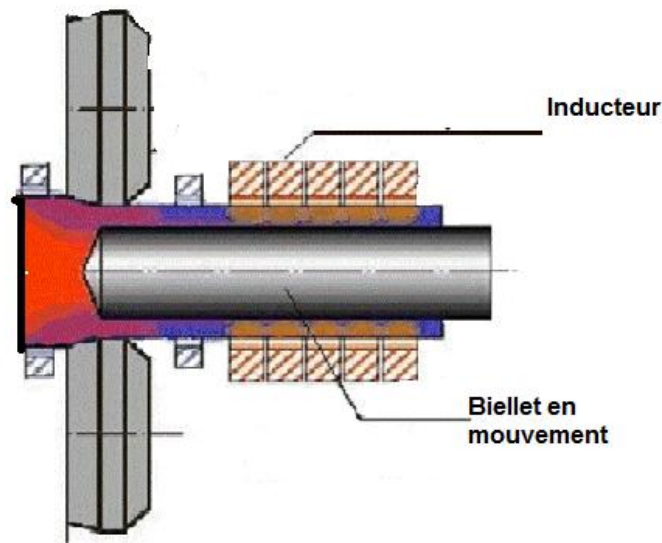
Chauffage avant formage des pièces conductrices en mouvement
